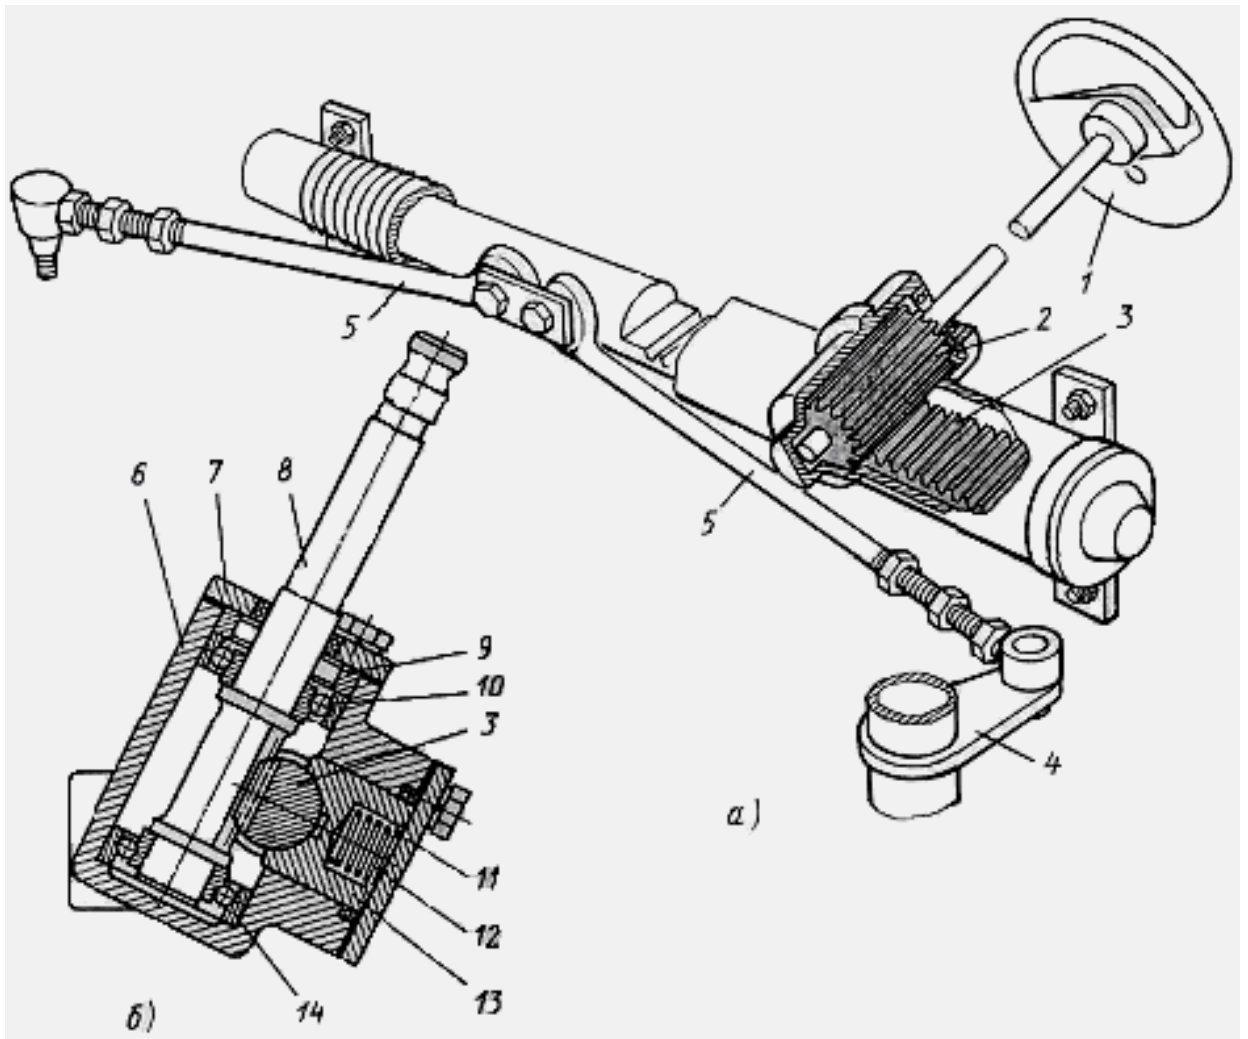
Рулевое управление с реечным механизмом: а - схема рулевого управления; б - реечный рулевой механизм; 1 - рулевое колесо; 2 - шестерня; 3 - рейка; 4 - поворотный рычаг; 5 - рулевая тяга; 6 - картер; 7 - верхняя крышка; 8 - рулевой вал; 9 - кольцо; 10, 14 - упорный подшипник; 11 - боковая крышка; 12 - пружина; 13 - упор
